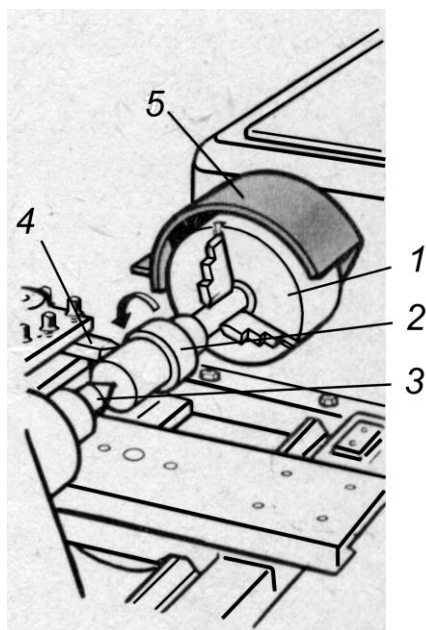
Схема закрепления заготовки в патроне с поджатием центром задней бабки:
